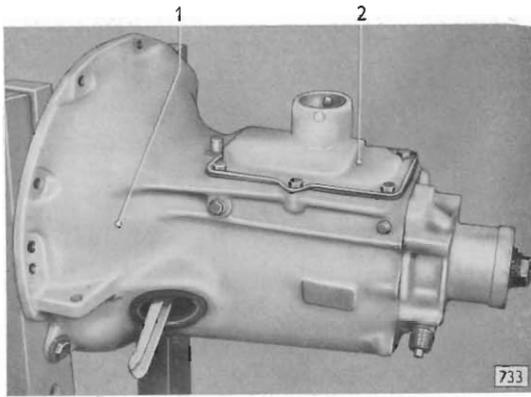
Getriebegehäusedeckel an Getriebegehäuse
